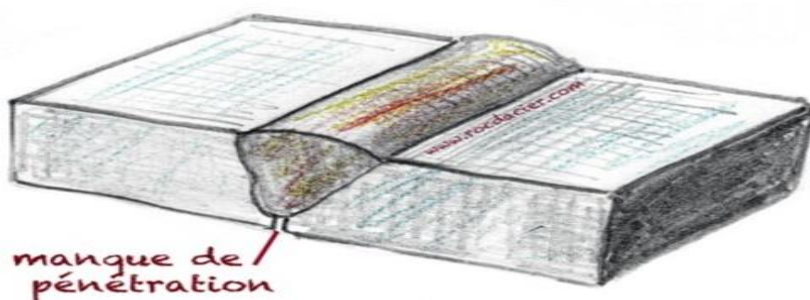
Manque de pénétration dans un cordon de soudure (Réf.[R28])
